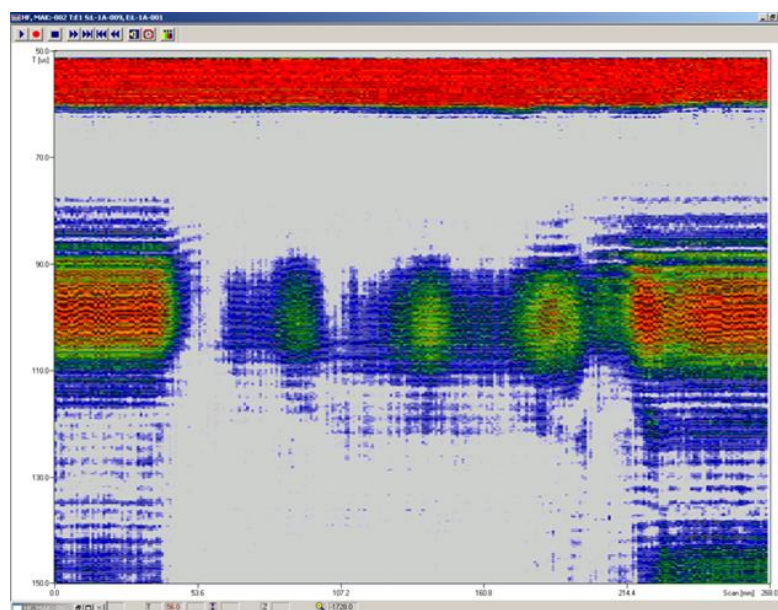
Ungenügende Durchschweißung und Schlauchporen entlang der Schweißnaht
